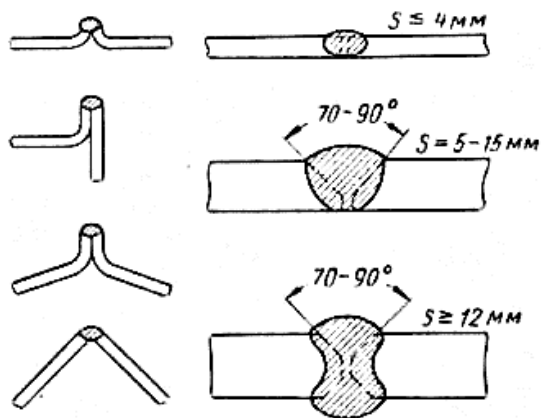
Форма з'єднань, що застосовуються при газовому зварюванні
